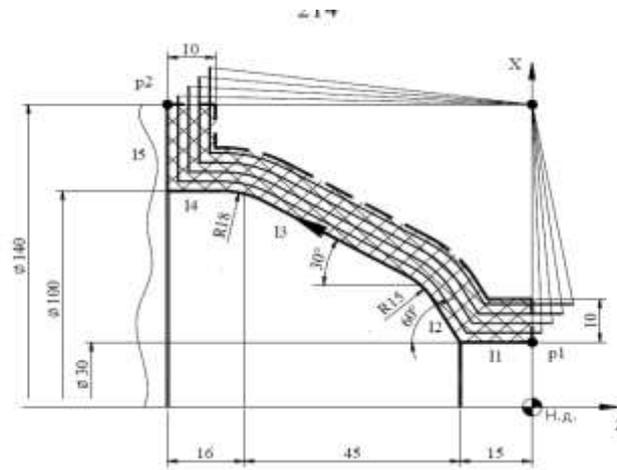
Схема удаления припуска при черновой обработке параллельной профилю
